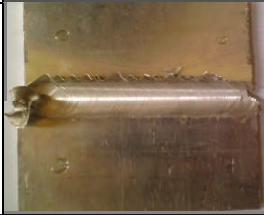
Prinsip *Friction Stir Welding* (Sumber: Thakasima, 2002)
